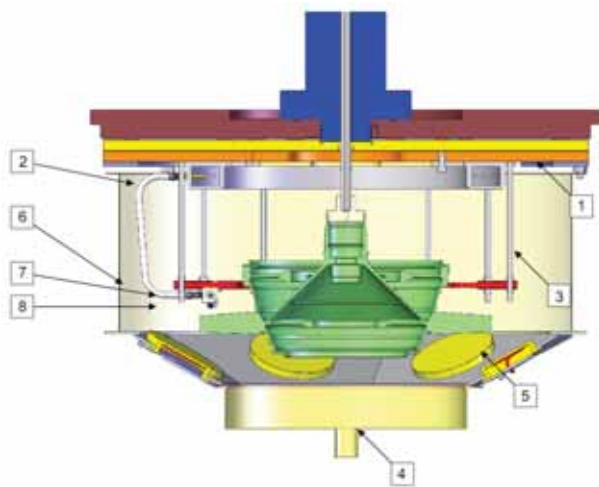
Система возбуждения колебаний струями масла: 1 – установочная плита; 2 – маслопровод; 3 – вспомогательная камера; 4 – масляный резервуар; 5 – нагревательное устройство; 6 – оснастка для крепления возбуждителей; 7 – блоки форсунок; 8 – форсунки
